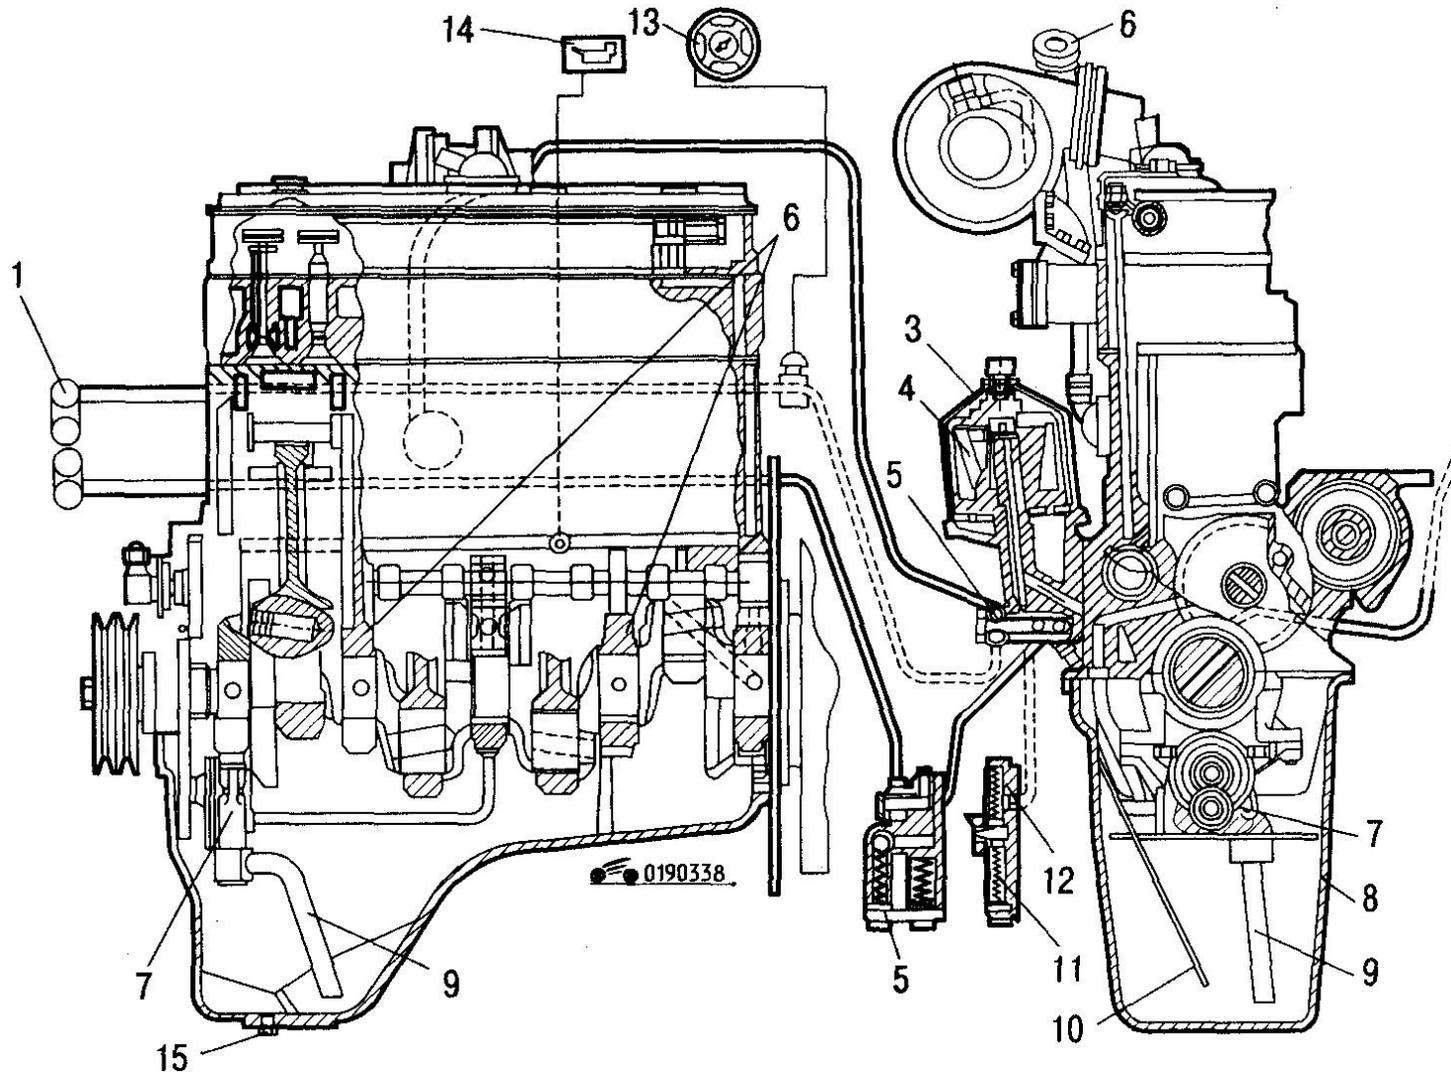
Схема системы смазывания: 1 - масляный радиатор; 2 - форсунки охлаждения поршней; 3 - центробежный масляный фильтр (центрифуга); 4 - защитная фильтрующая сетка; 5 - предохранительный клапан; 6 - маслосливная горловина; 7 - масляный насос; 8 - масляный картер; 9 - маслозаборная трубка; 10 - указатель уровня масла; 11 - сливной клапан центрифуги; 12 - редукционный клапан центрифуги; 13 - указатель давления масла; 14 - сигнализатор аварийного давления масла; 15 - сливная пробка
